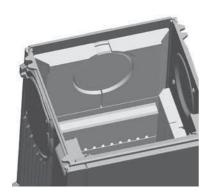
Pose des pierres arrière haut droite (H2.1-11R) et arrière haut gauche (H2.1-11L) – le cas échéant, pose de la pierre de raccord (H2-10) (selon raccordement)
